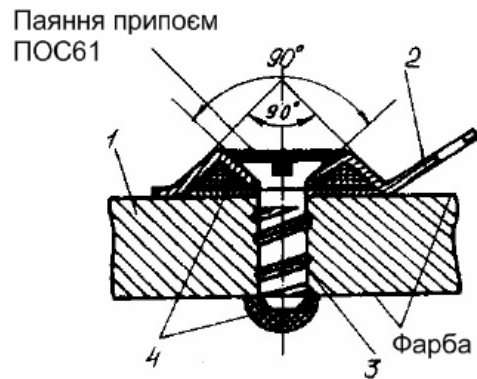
Приєднування пелюстки до литого корпусу самонарізними гвинтами: 1 – корпус; 2 – пелюстка; 3 – гвинт; 4 – компаунд ЕЗК-6
